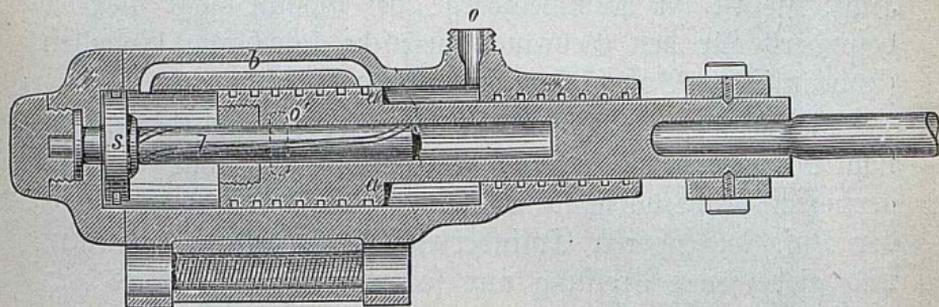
Bohrmaschine von Darlington: Grundriß.
